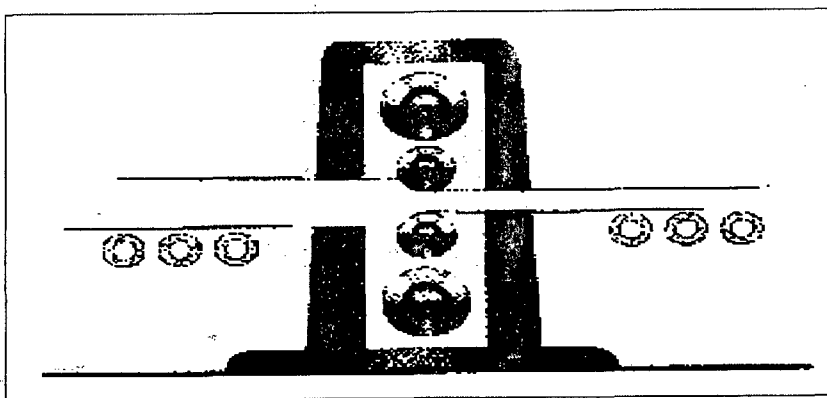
Esquema do processo de laminação a quente para os aços destinados a armaduras para concreto armado (DIAS, 1998)
